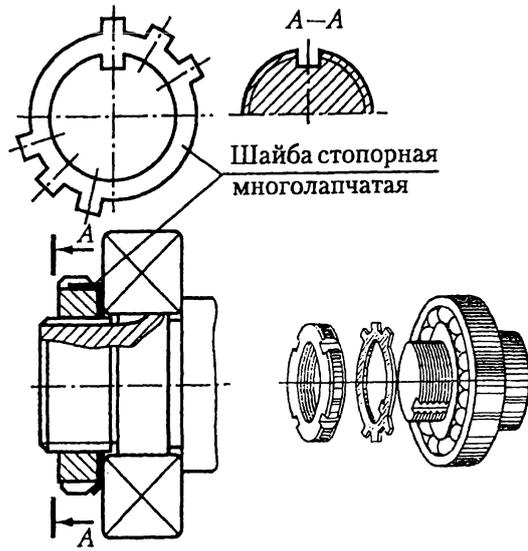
Круглая шлицевая гайка со стопорной многолапчатой шайбой
